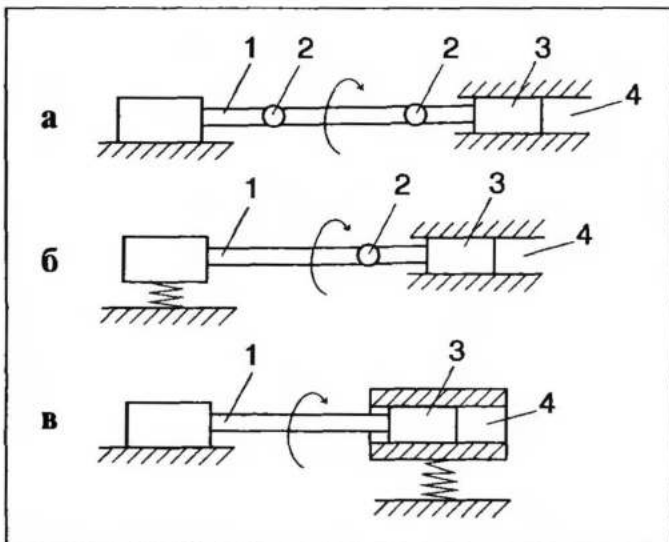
Схемы взаимного расположения шпинделя хонинговального станка и детали:
